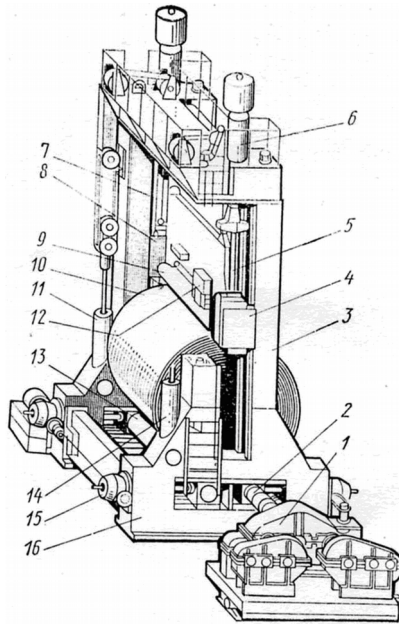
Машина для изготовления рулонированных обечайек: 1 – привод рабочего вала; 2, 13 – опорные валки; 4, 8 – опоры-траверсы; 5 – сменные проставки; 6 – силовые гидроцилиндры; 7 – траверсы; 9 – рабочий валок; 10 – рулонированная обечайка; 11, 14 – приводы перемещения траверсы; 12 – поджимные опорные ролики; 15 – привод раздвижения валков; 16 – станина
